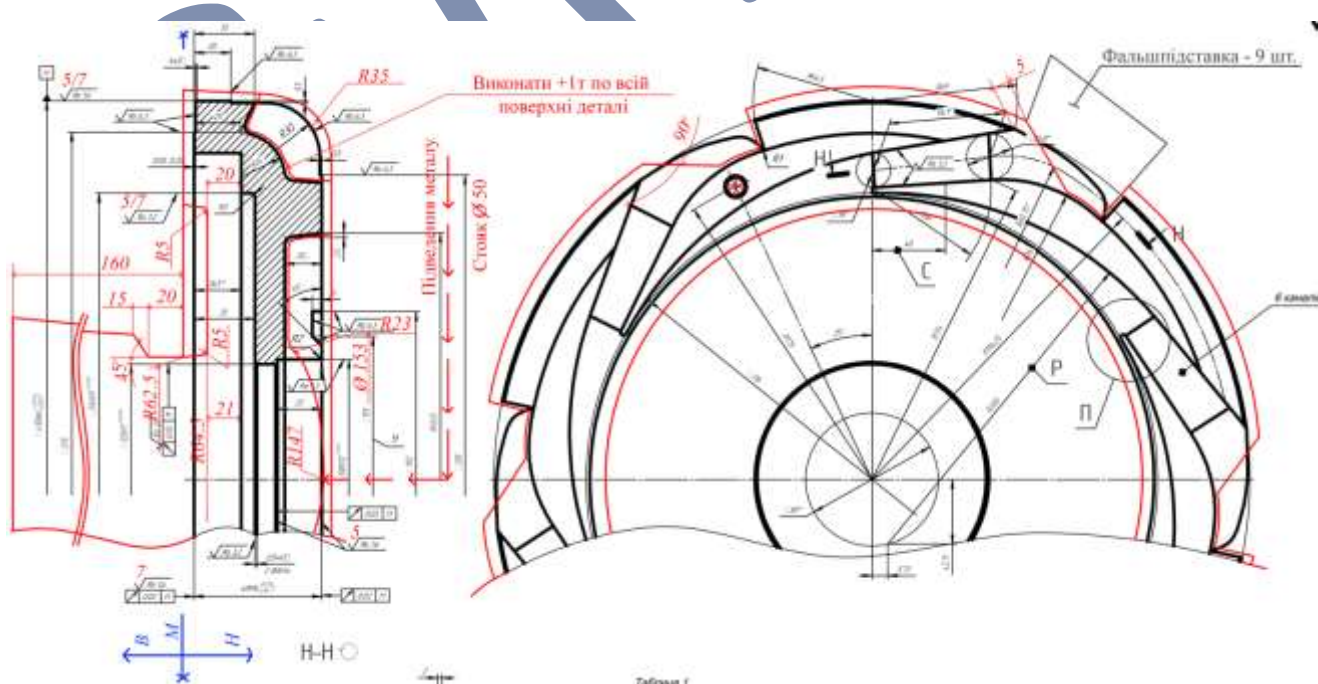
Розмітка ливарного варіанту креслення
